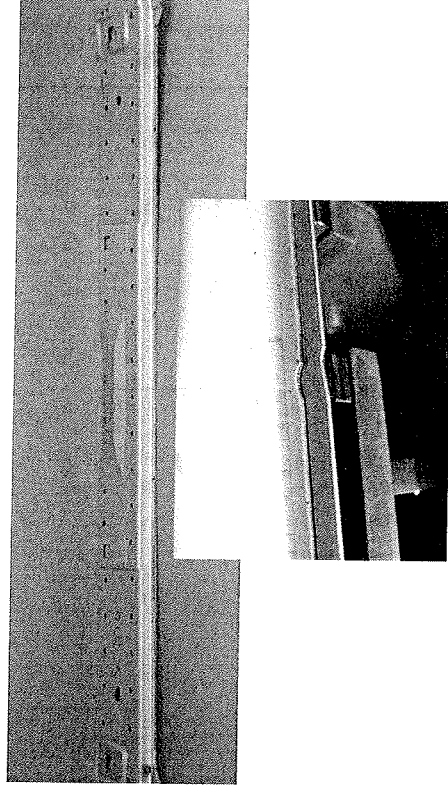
Realbauteil zur Evaluierung des Gesamtsystems: Dachquerträger Baureihe 211.
